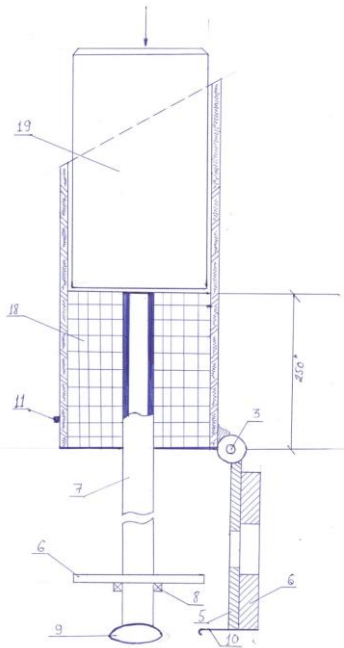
Боковой разрез цилиндрического корпуса пресса в состоянии завершения прессования брикета.
